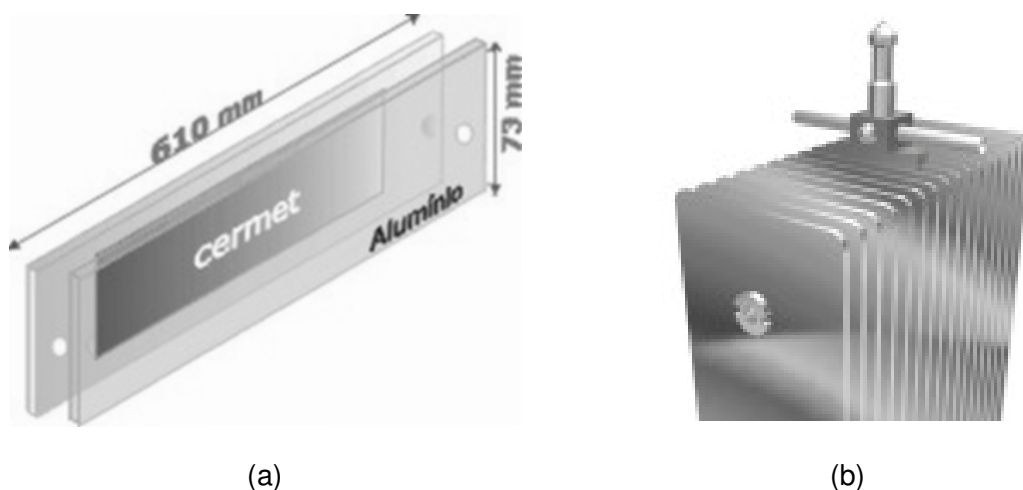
(a) Placa combustível; (b) Elemento combustível.
